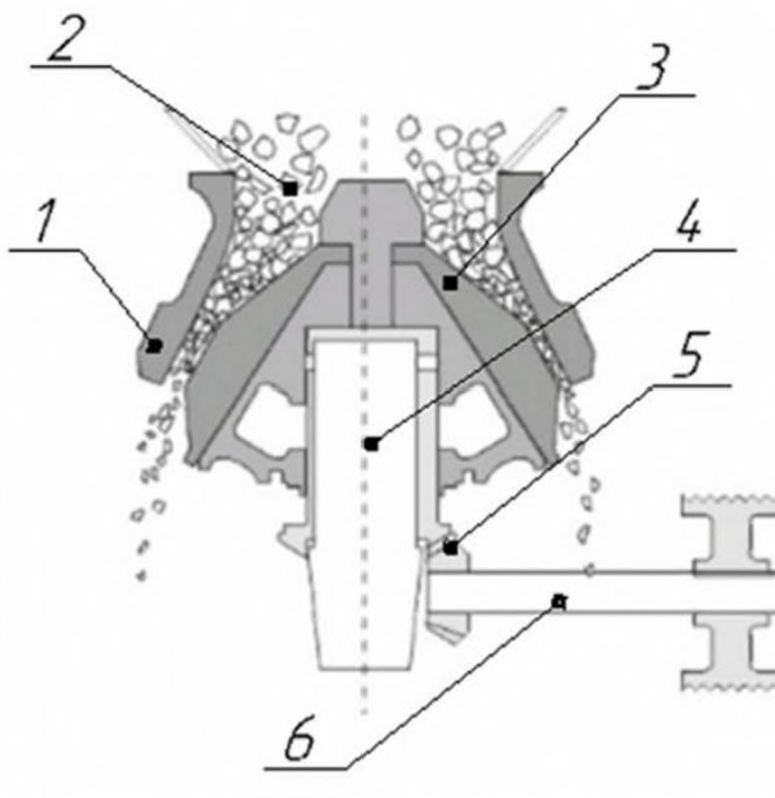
Пружинна дробарка: 1 – верхній ударний кожух; 2 – матеріал, 3 – конус; 4 – центральний вал; 5 – зубова конічна передача; 6 – привід
